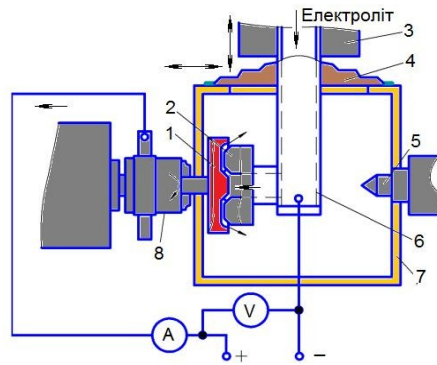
Схема установки для виконання токарних операцій: 1 – деталь; 2 – електрод-інструмент; 3 – патрон; 4 – мідний диск; 5 – центр; 6 – штанга; 7 – камера; 8 – передня бабка
